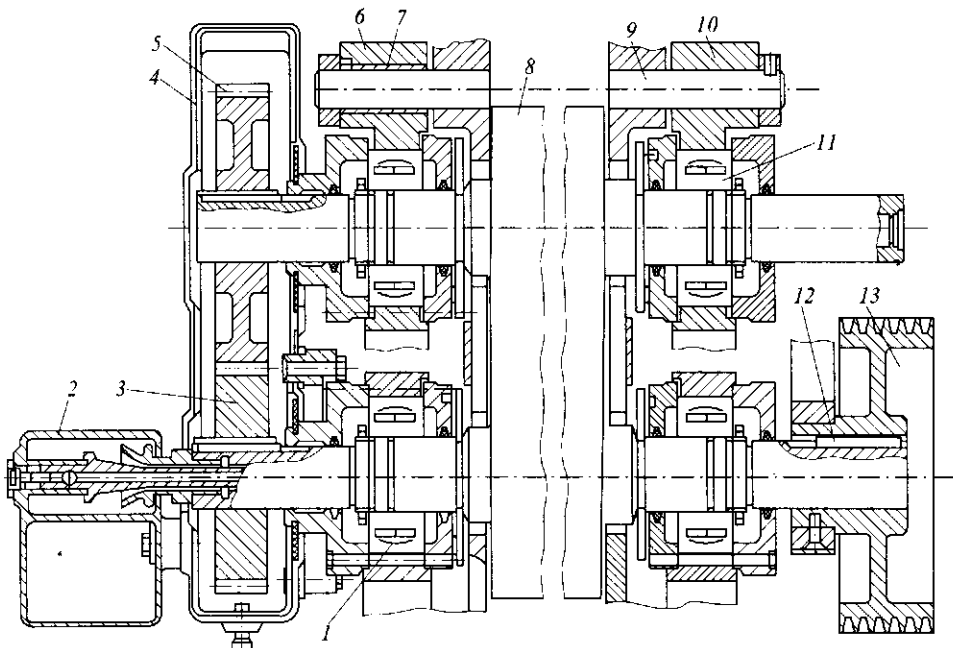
Мелющие валцы с подшипниковыми узлами, приводом и межвальцовой передачей
